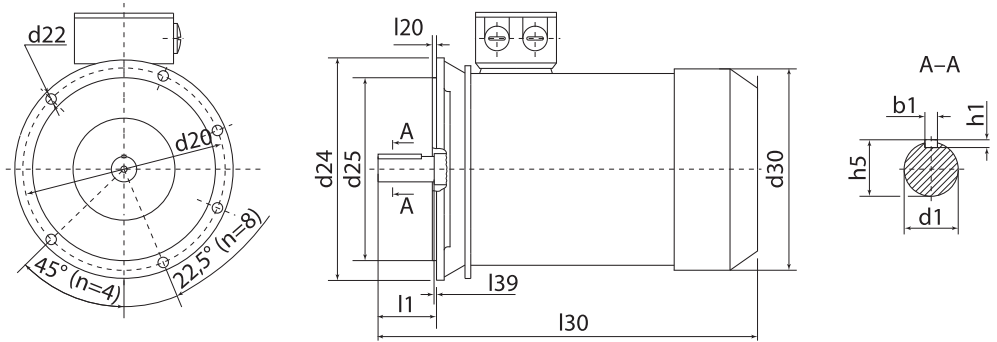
Габаритные и установочные размеры (исполнение 3081)
